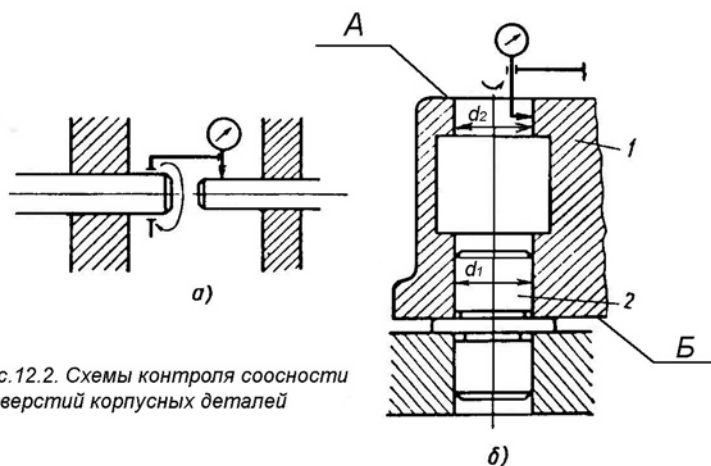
Схемы контроля соосности отверстий корпусных деталей
